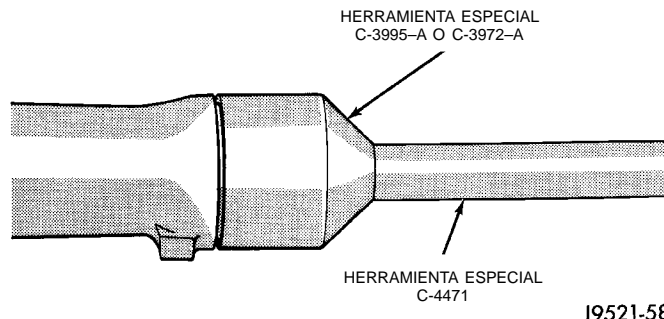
Instalación de la junta de la cubierta de sobremarcha
